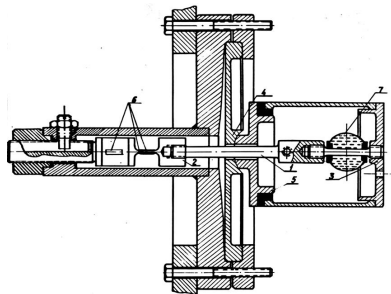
Нагружающее устройство: 1 – переходник; 2 – винтовой захват; 3 – неподвижная опора; 4 – упругий элемент; 5 – сферическая опора; 6 – тензодатчики проволоочные; 7 – баллон с агрессивной средой
